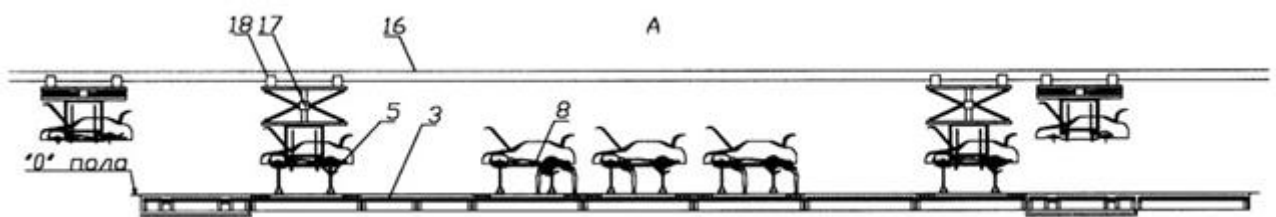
Вид на участок стыковки и сборки шасси с кузовом
